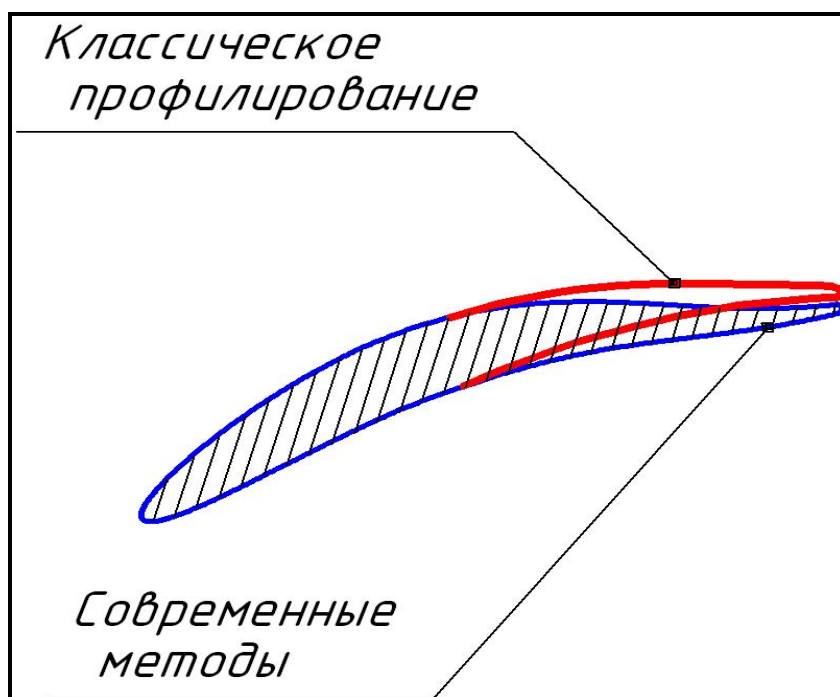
Профили компрессорной решетки, полученные различными методами профилирования.
